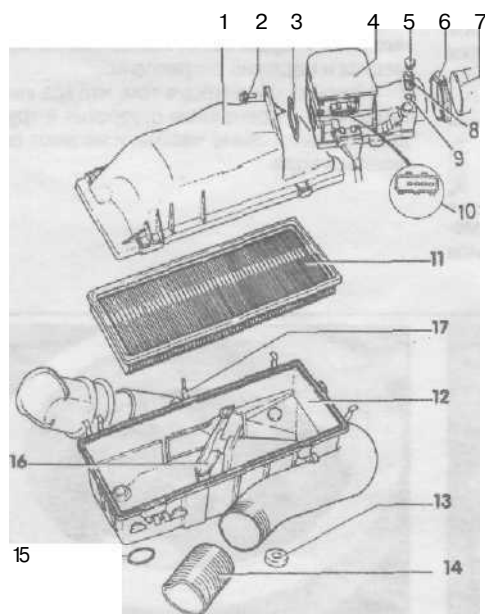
Детали воздухоочистителя - система впрыска топлива Digijet
